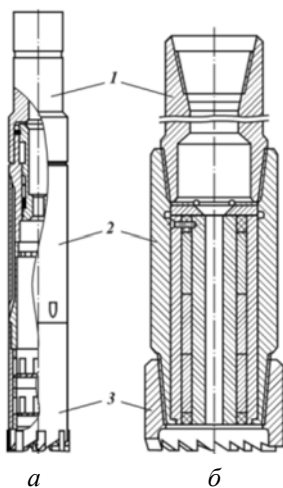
Устройства очищающие типа УОЗС и УОЗ1: 1 – переводник; 2 – корпус; 3 – головка с зубцами
